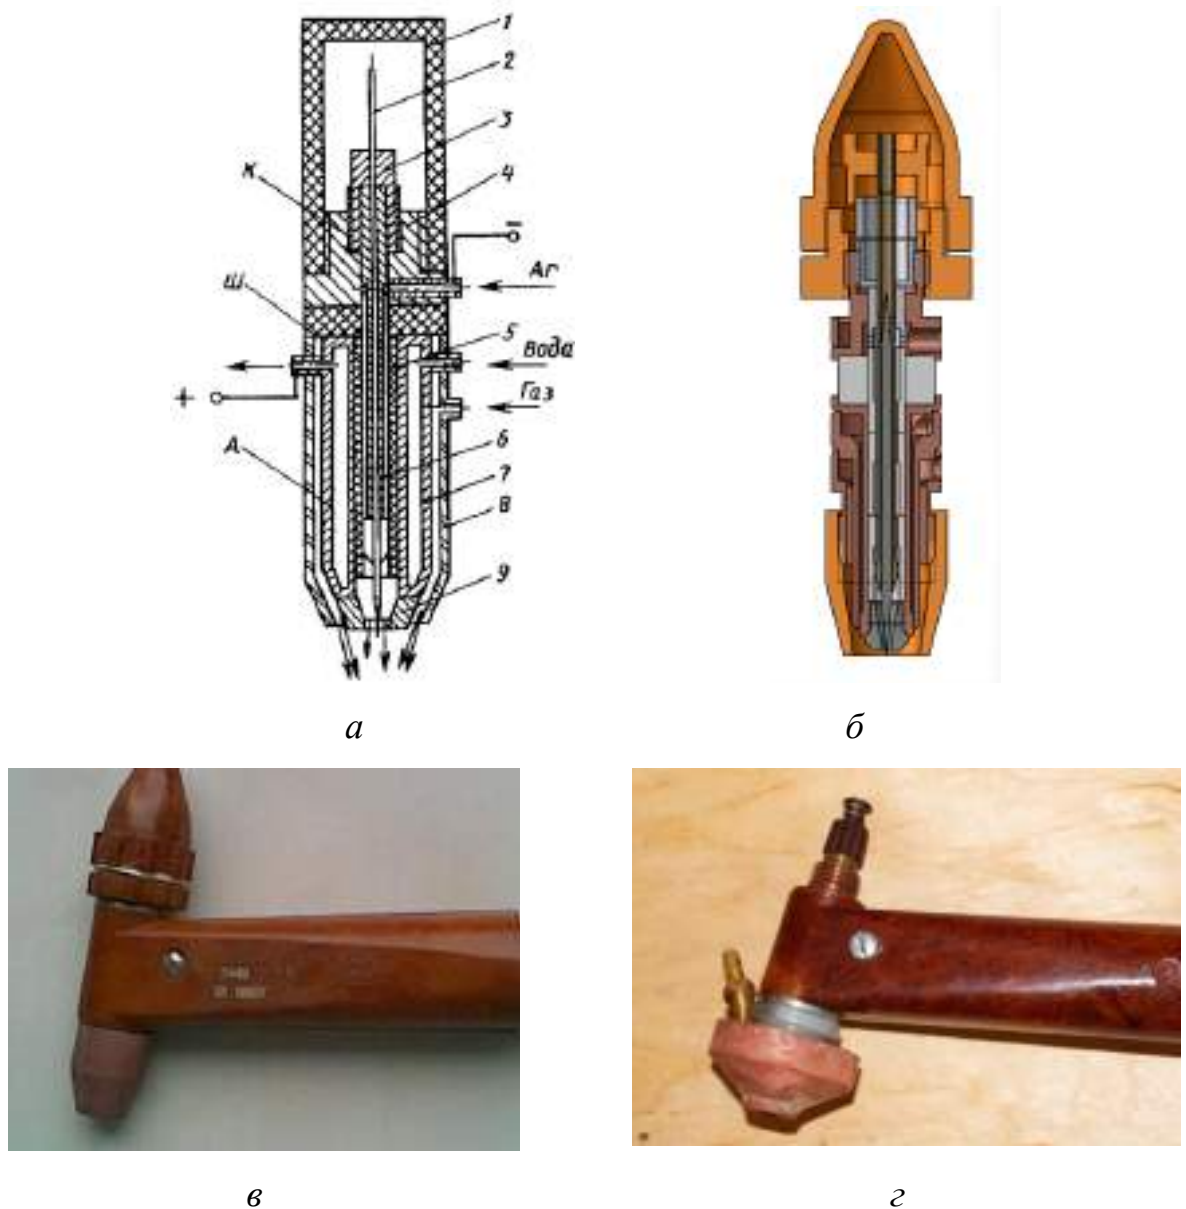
Схема (а), переріз (б) та загальний вигляд (в) плазмотрона МПУ-4 для мікроплазмового зварювання та загальний вигляд цього плазмотрона з сопловим вузлом для введення порошку в струмінь (з), модернізованого для комплектації універсального лабораторного комплексу для дослідження адитивних технологій наплавлення.
